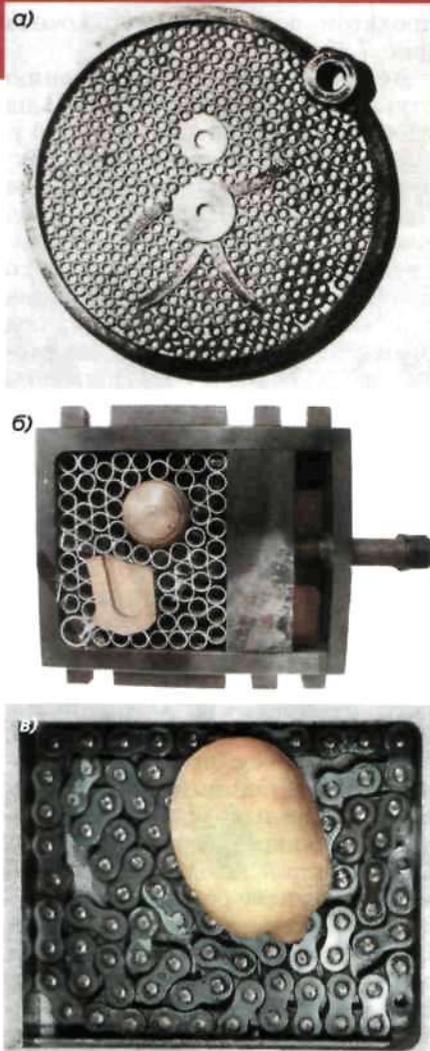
Устройства для крепления деталей сложной формы кольцами — а), б) и цепью — в)
